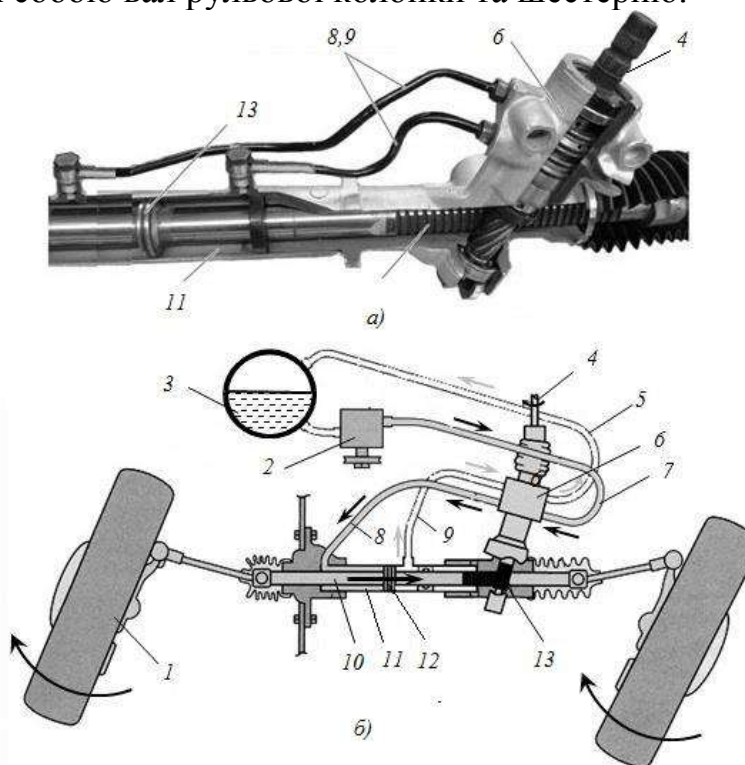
Розріз вузла (а) та схема будови (б) рульового керування з гідропідсилювачем:
